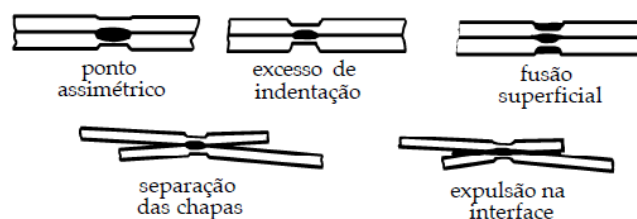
Defeitos observados no Processo de Soldadura por Pontos [29].
